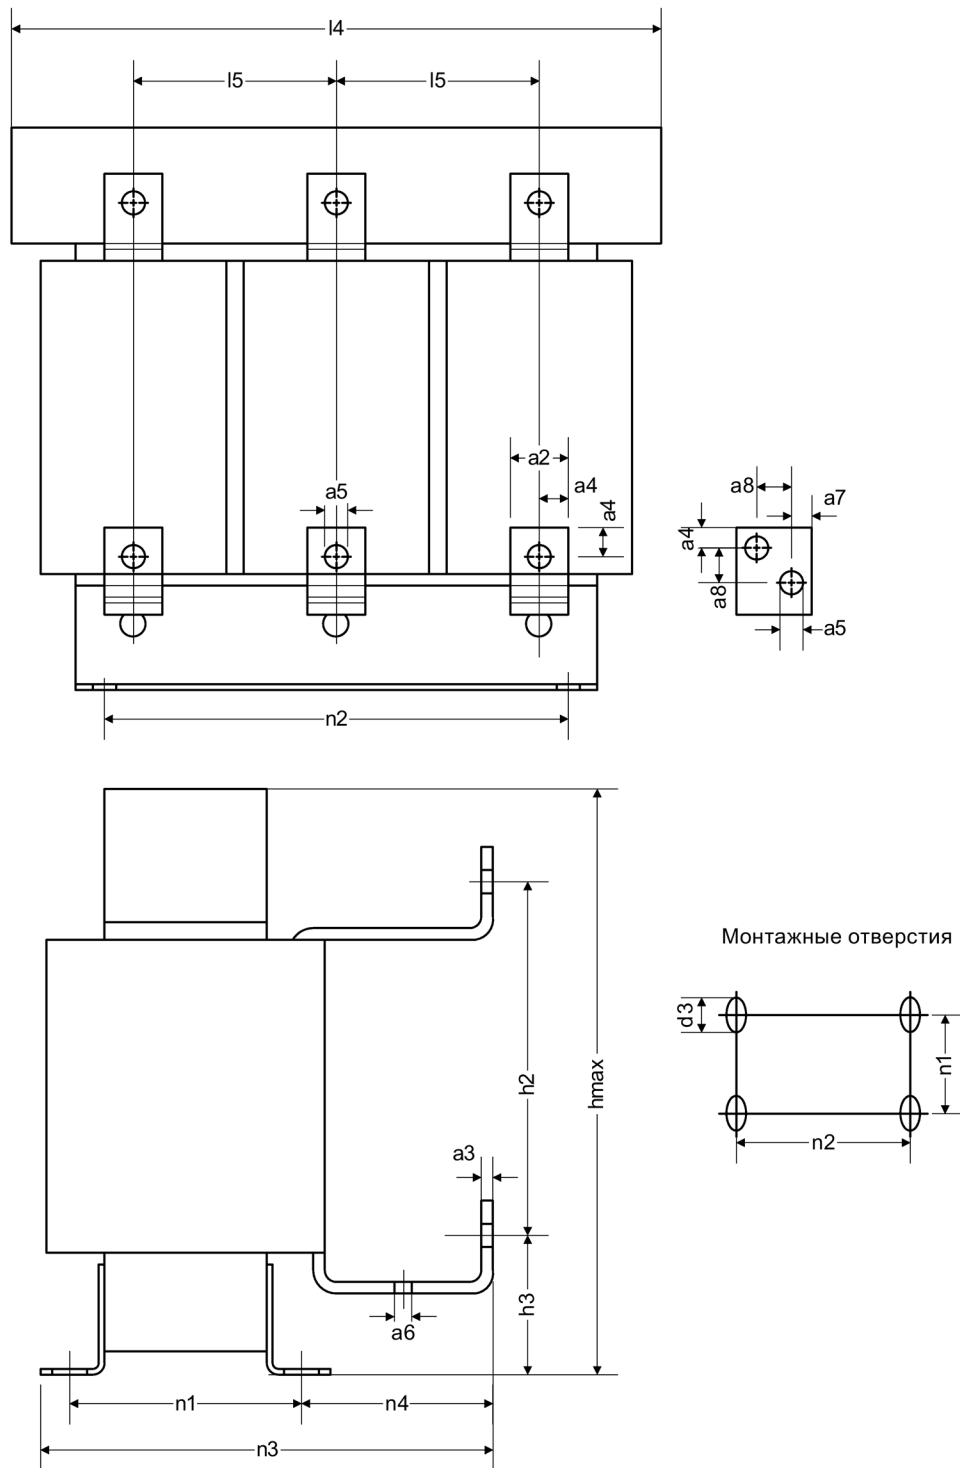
Габаритный чертеж дросселя du/dt
